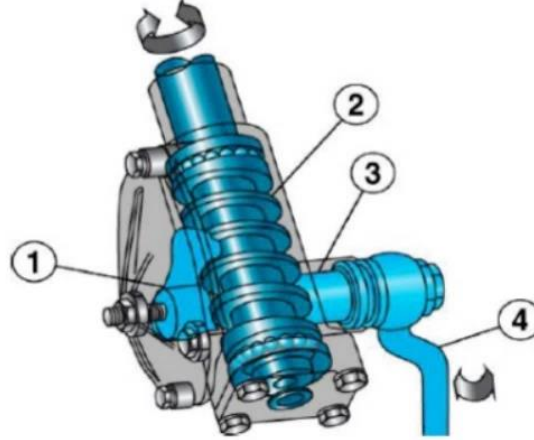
Tornillo sinfín y dedo. Componentes: (1) Dedo de rodadura (2) Tornillo sinfín cilíndrico (3) Eje de la biela de mando (4) biela de mando de la dirección. [8]
